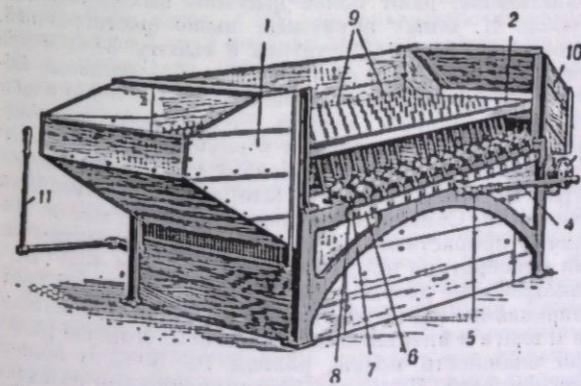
Трясилка ТК: 1 — загрузочная воронка; 2 — решётка; 3 — приводной диск главного вала; 4 — шатун; 5 — головка шатуна; 6 — соединительное дышло; 7 — кривошип; 8 — игольчатый валик; 9 — иглы; 10 — выпускная часть; 11 — валик отводки.
